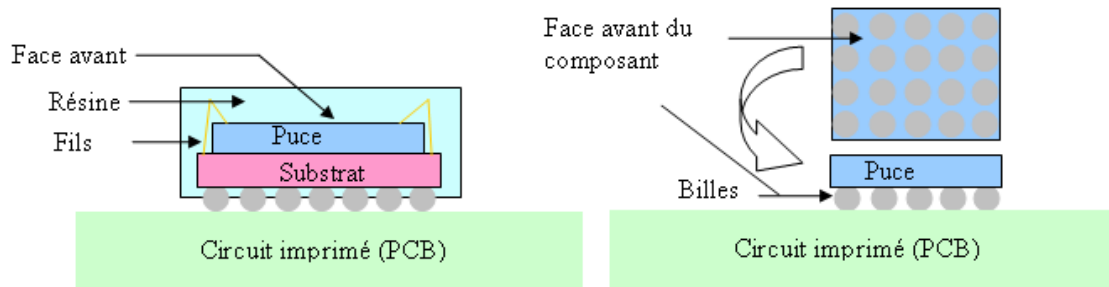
a) Assemblage de type BGA - b) Assemblage de type WL-CSP
